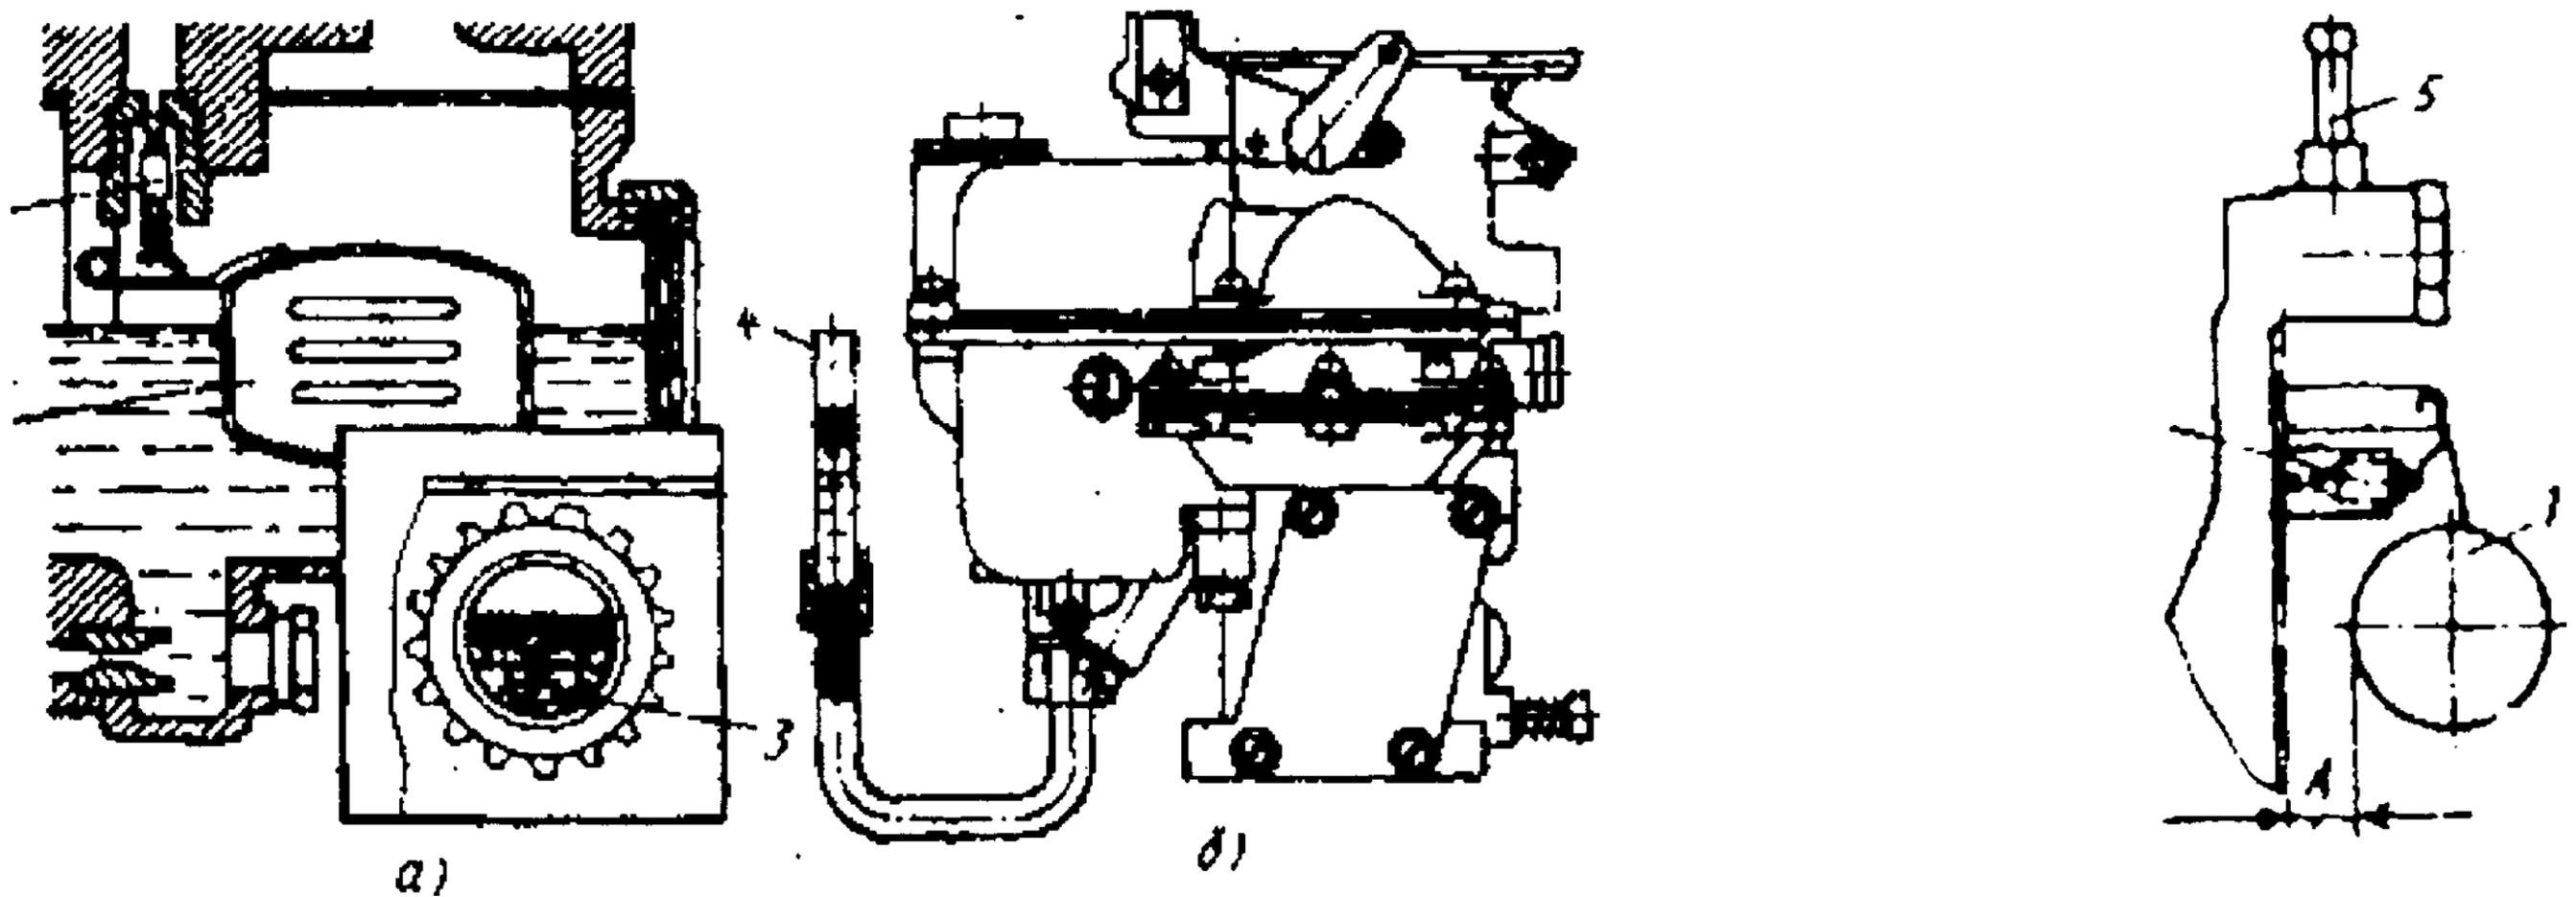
Схемы проверки и регулировки уровня бензина в поплавковой камере карбюраторов:
